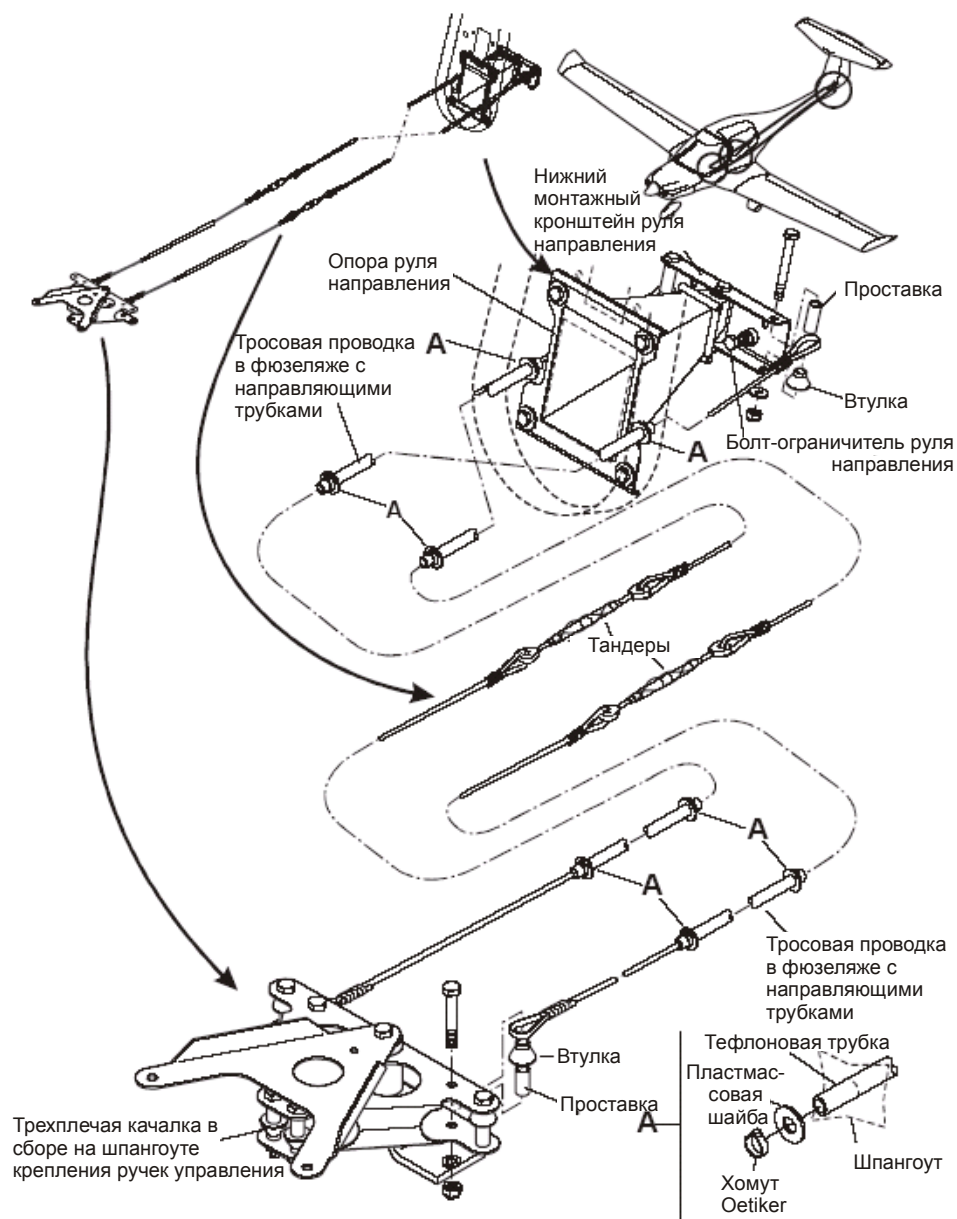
Схема установки элементов системы управления рулем направления в хвостовой части фюзеляжа
